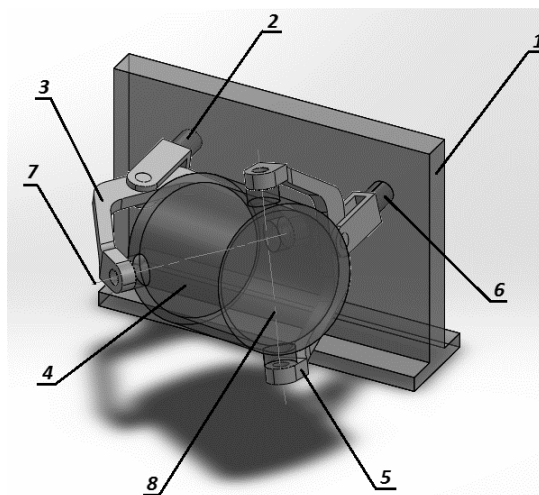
Схема змішувача з тривимірним обертанням робочої ємкості: 1 – корпус машини, 2 – вхідний (ведучий) вал, 3 – вилка № 1, 4 – робоча ємкість (циліндричний барабан), 5 – вилка № 2, 6 – вихідний (ведений) вал
